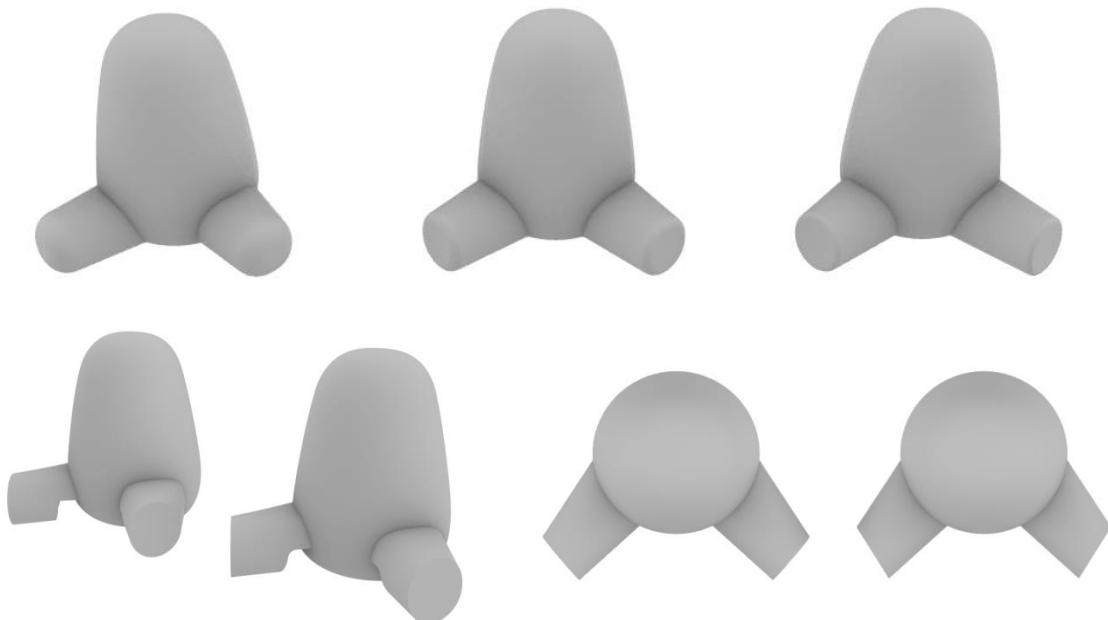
Vizualizace nohou robota a jeho řezů,
